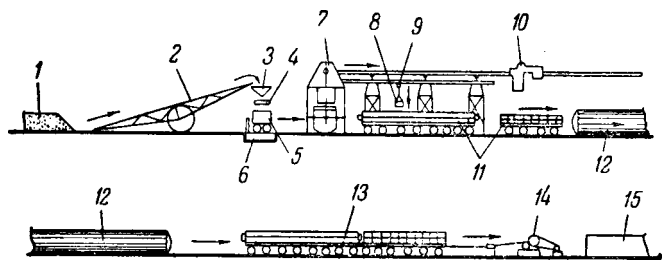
Технологическая схема производства термоизоляционных оболочек из автоклавного армопенобетона для покрытия подземных теплопроводов.
